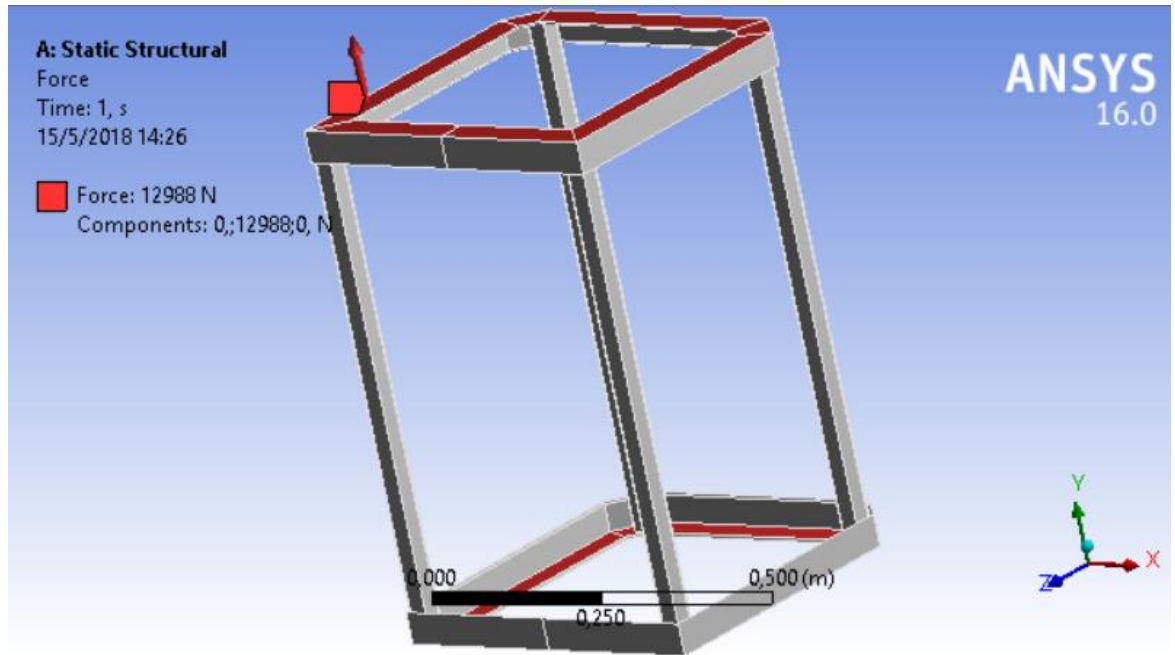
7 Aplicación de las cargas a la estructura [Autor]
